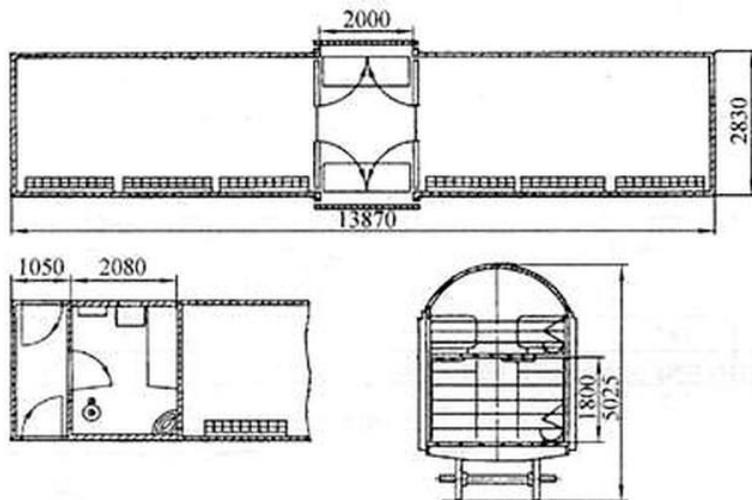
Двухъярусный крытый вагон для перевозки скота
